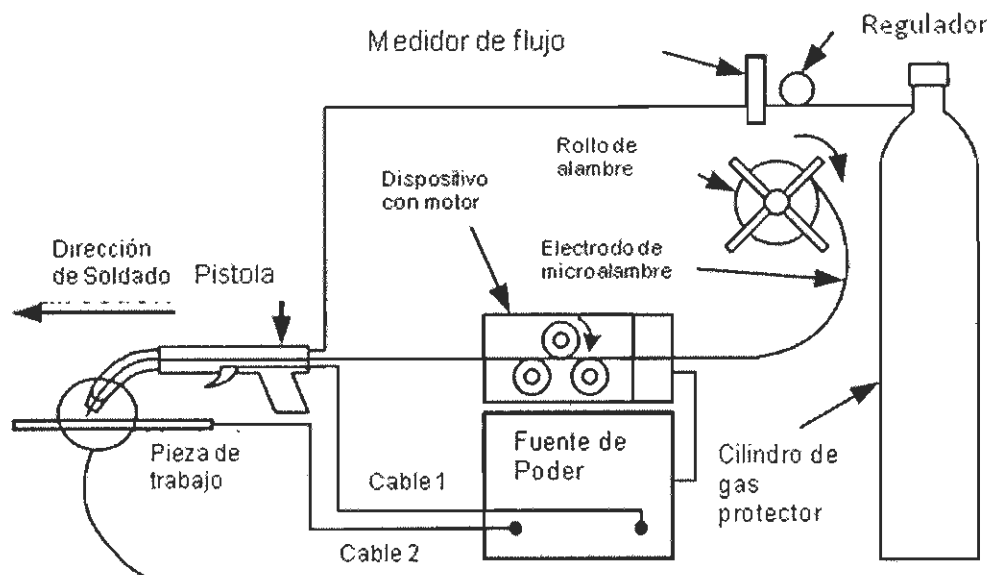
Esquema del proceso por soldadura GMAW [2].
